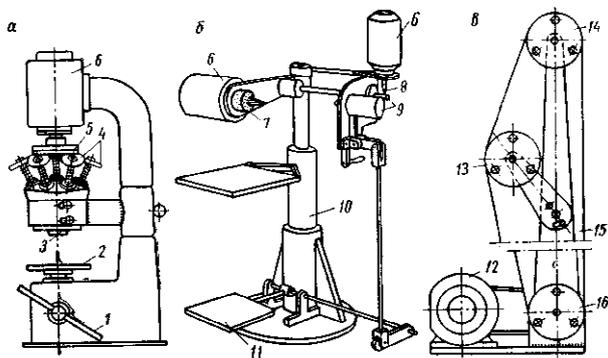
Станки для механизированной обработки и зачистки изделий:
